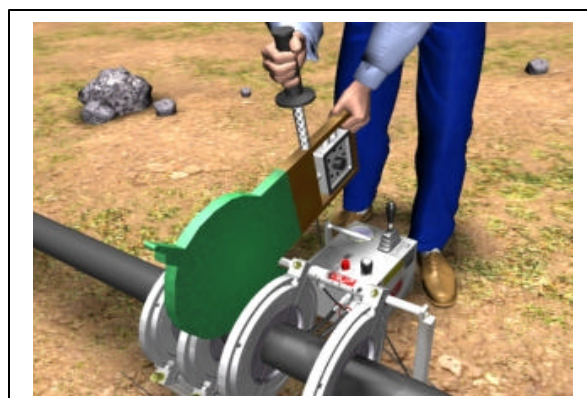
Quando a temperatura da placa de aquecimento estiver no valor recomendado pelo fabricante do tubo, a mesma deverá ser posicionada, mantendo-se a pressão de solda até a formação de um cordão inicial entre a placa e o tubo.
